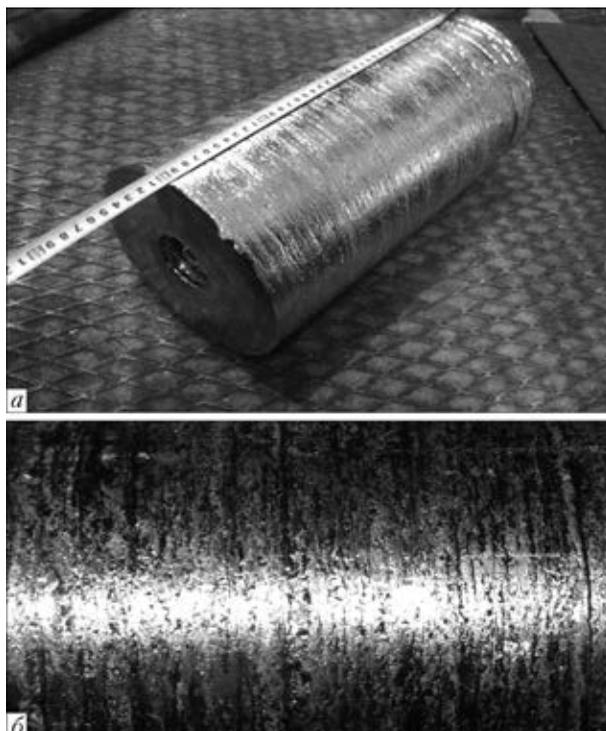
Внешний вид (а) и наружная поверхность (б) полого слитка после плавки
